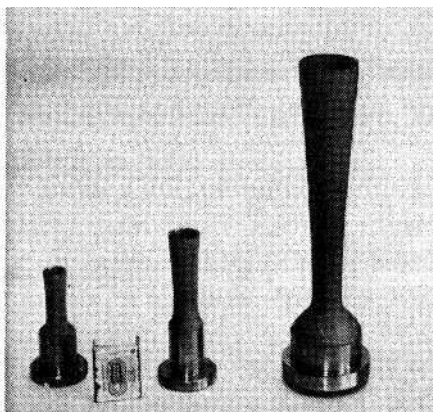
Сопла насосов, изготовленных методом плазменного формообразования.
